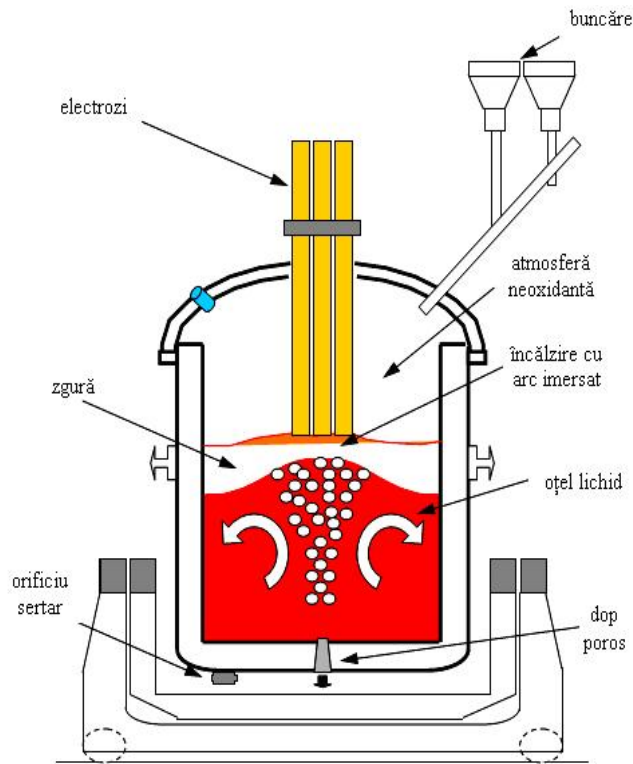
Schema instalației Ladle Furnace (L.F.) [25]
